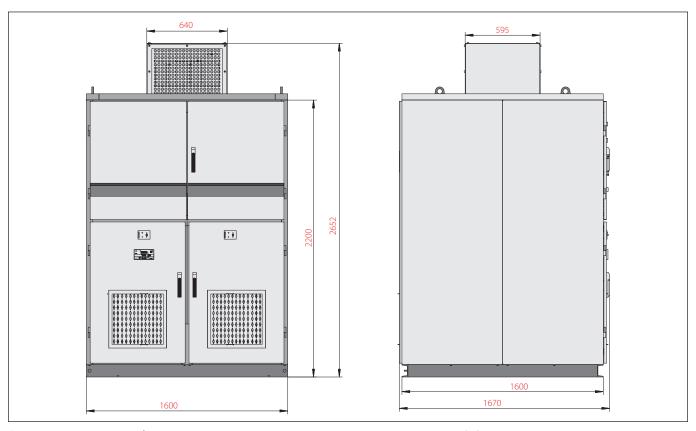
Корпус шкафа токоограничивающего реактора типоразмера EA03/EC03
